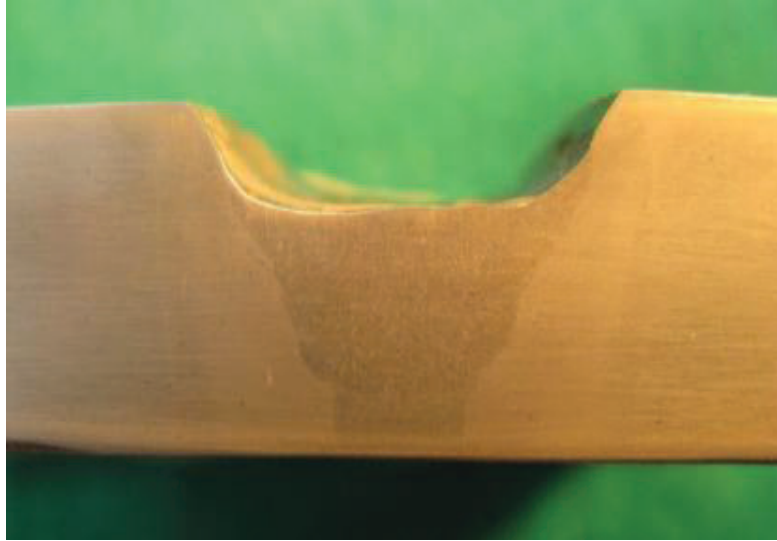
12 Macrografía del cordón de soldadura completado el primer pase (raíz) de soldadura realizado con proceso GTAW (6G), presenta buena penetración y fusión, 10X.
